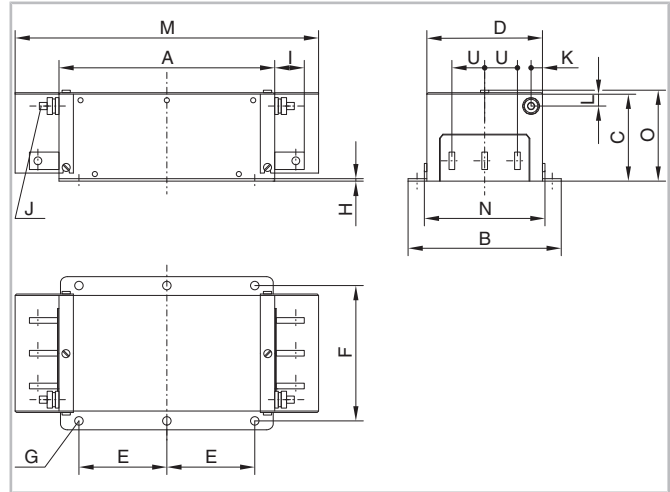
Габаритный чертеж RFI фильтров 3259-320-99 .. 3259-600-99
